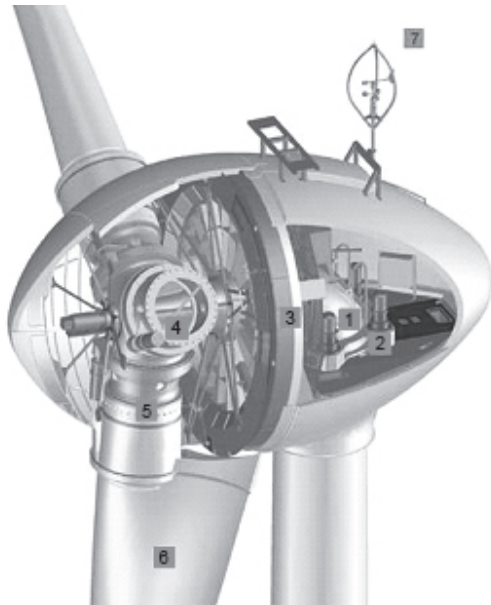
Componentes de um aerogerador de eixo horizontal.
